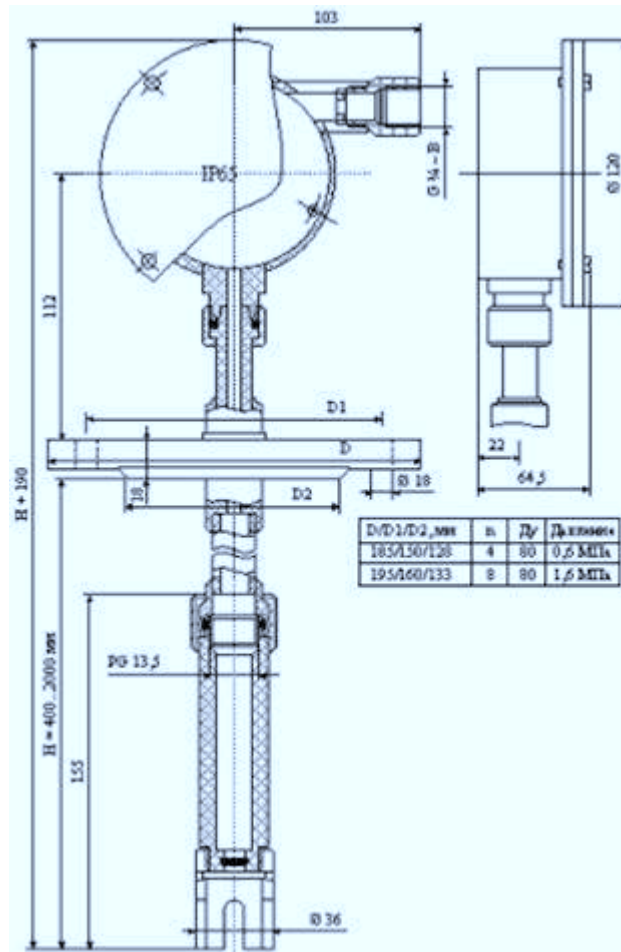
Габаритные и монтажные размеры первичного преобразователя рН-4121 типа Н с арматурой АРН-1.1 или АРТ-1.1
